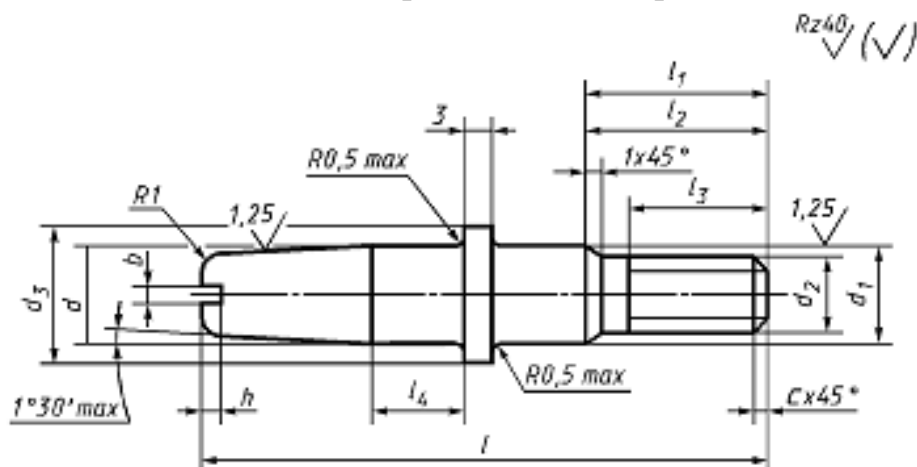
Конструкция центрирующих штырей с резьбовым хвостовиком
